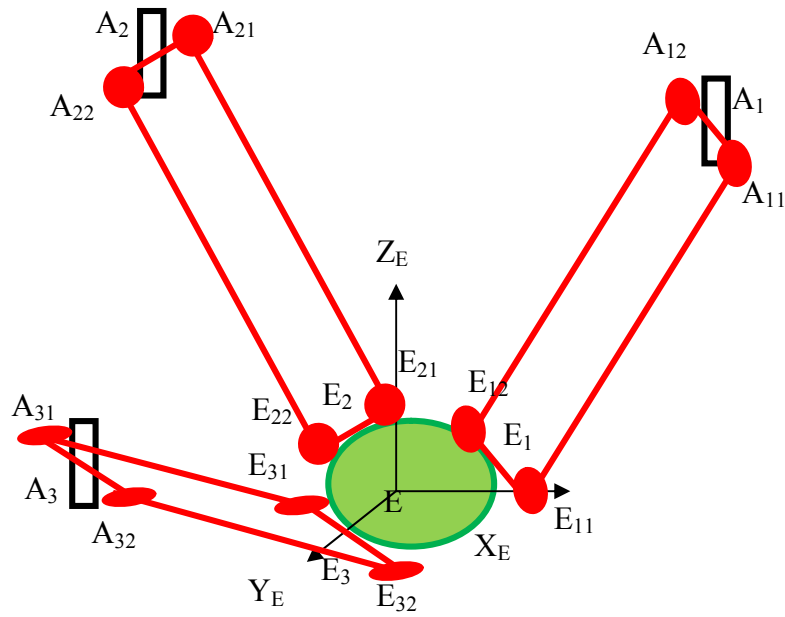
Paramétrage de la partie mobile de la machine-outil.
